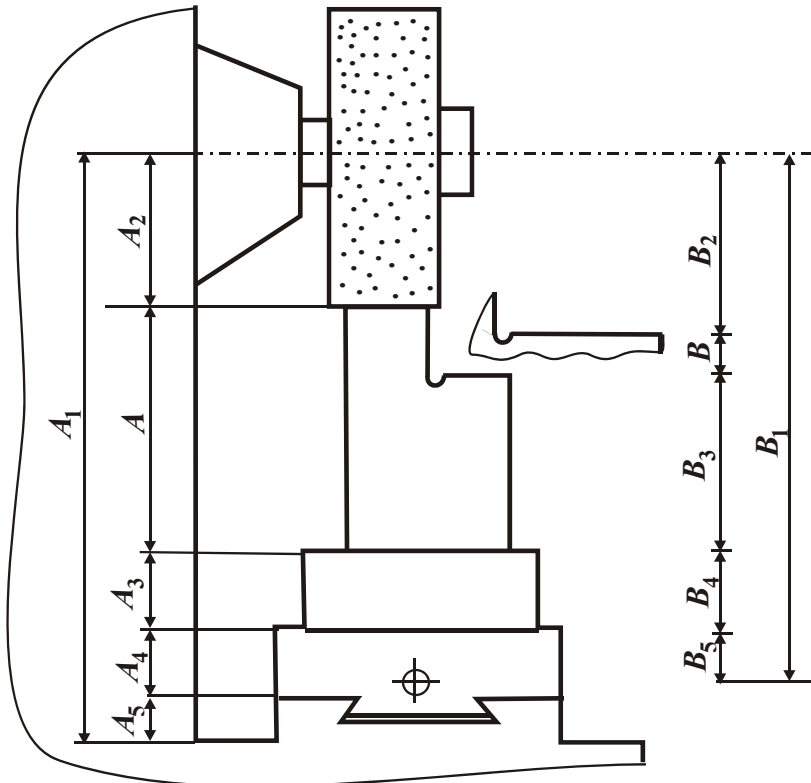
Схема обработки поверхностей и размерные цепи наладок.
